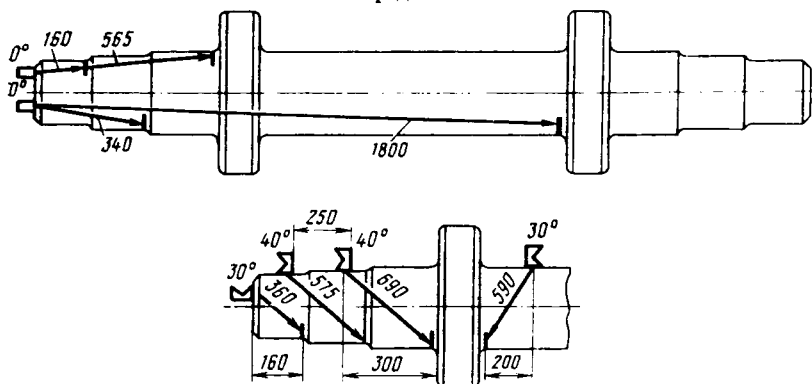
Схемы и зоны контроля прямым и наклонным искателями со стороны главного приводного вала эскалатора Н-40 очереди II
